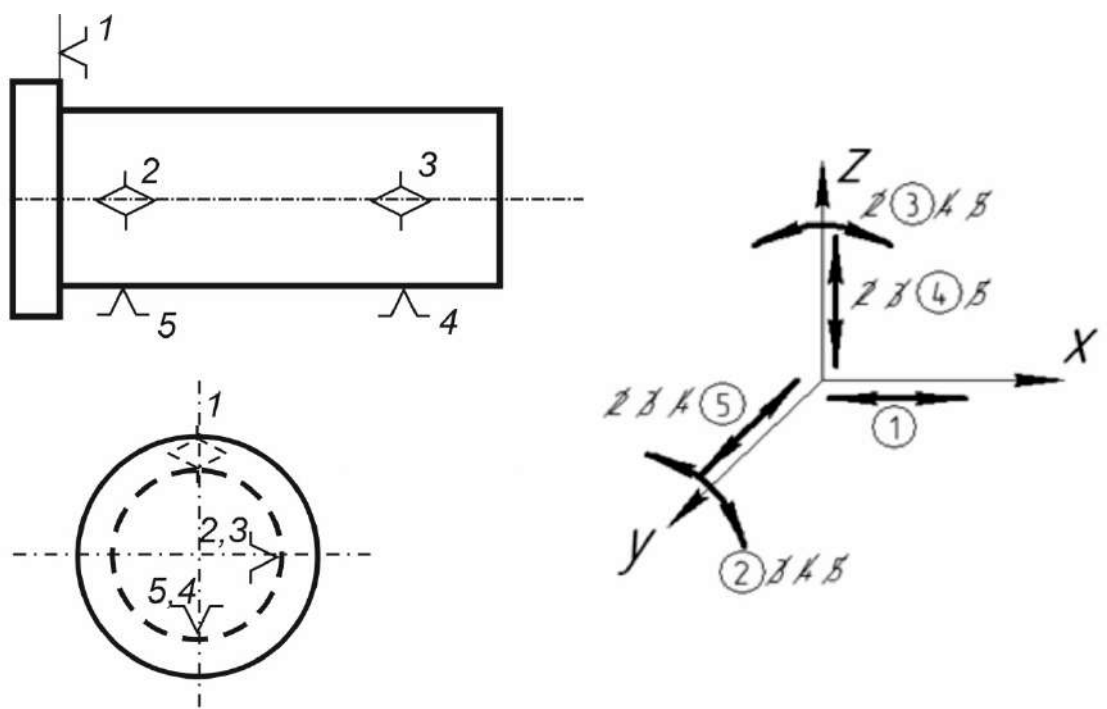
Базування циліндричної заготовки у втулці з упором у торець
